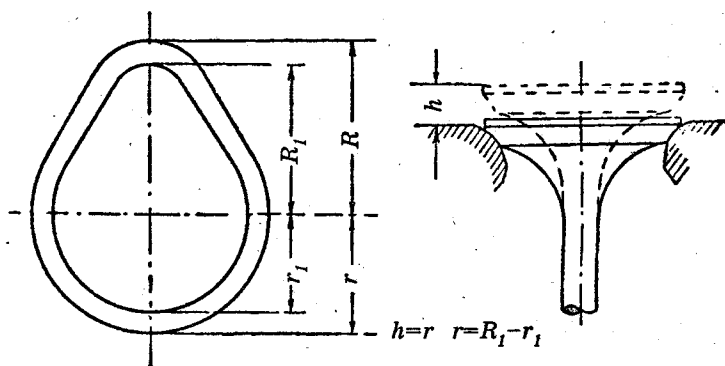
Схема, показывающая возможность восстановления профиля кулачка шлифованием
